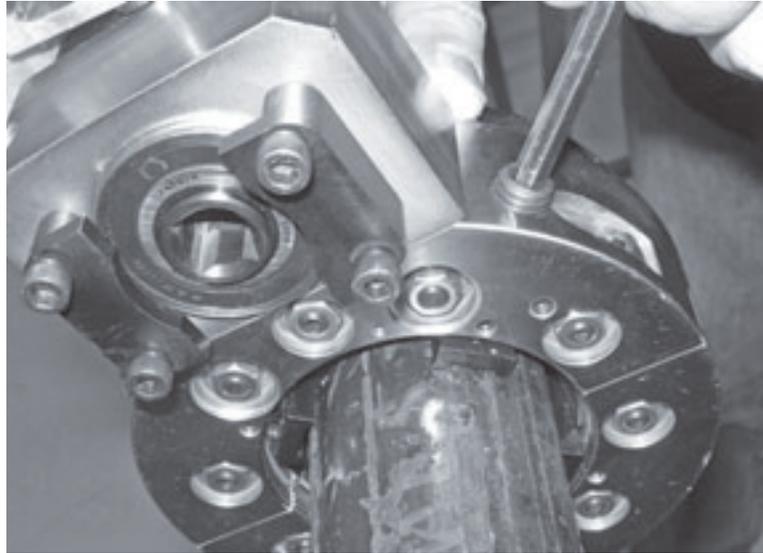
Apriete las zapatas de fijación como se muestra.
